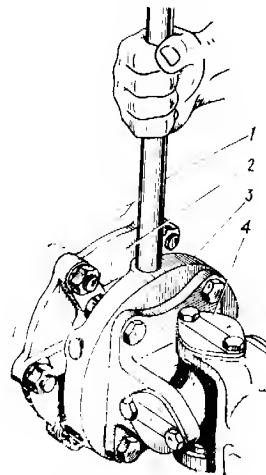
Проворачивание коленчатого вала с помощью специального приспособления:
